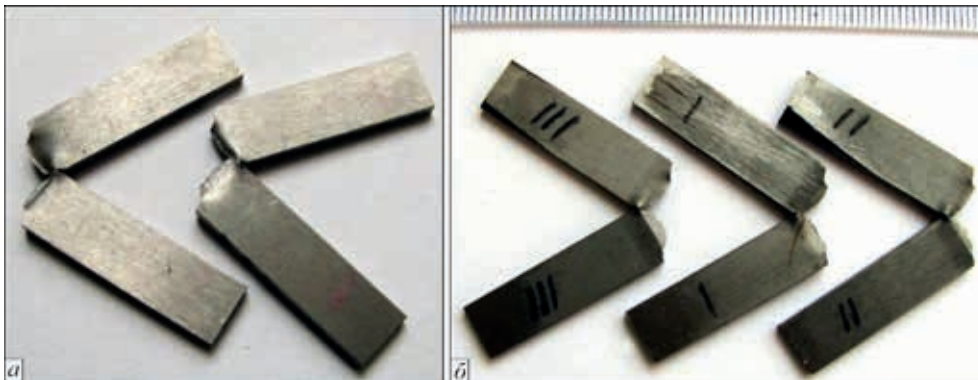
Зовнішній вигляд зруйнованих зразків: а – основний метал; б – зварне з'єднання
